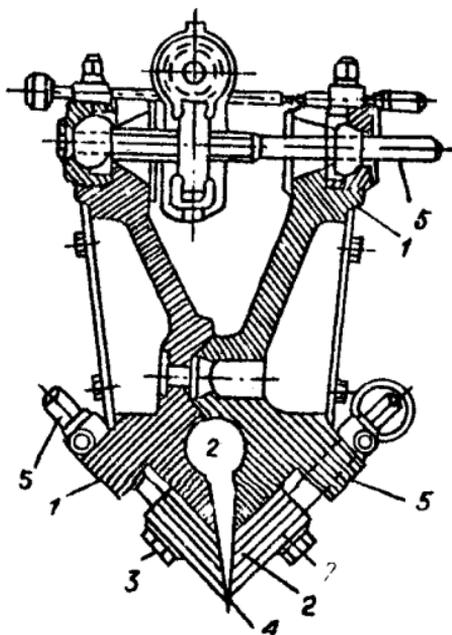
Фильера для формования пленки: 1 - корпус; 2 - полость фильеры; 3 - полированная пластина; 4 - зазор; 5 - регулировочные винты.
